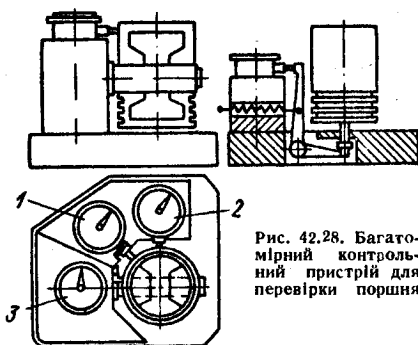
Багатомірний контрольний пристрій для перевірки поршня
